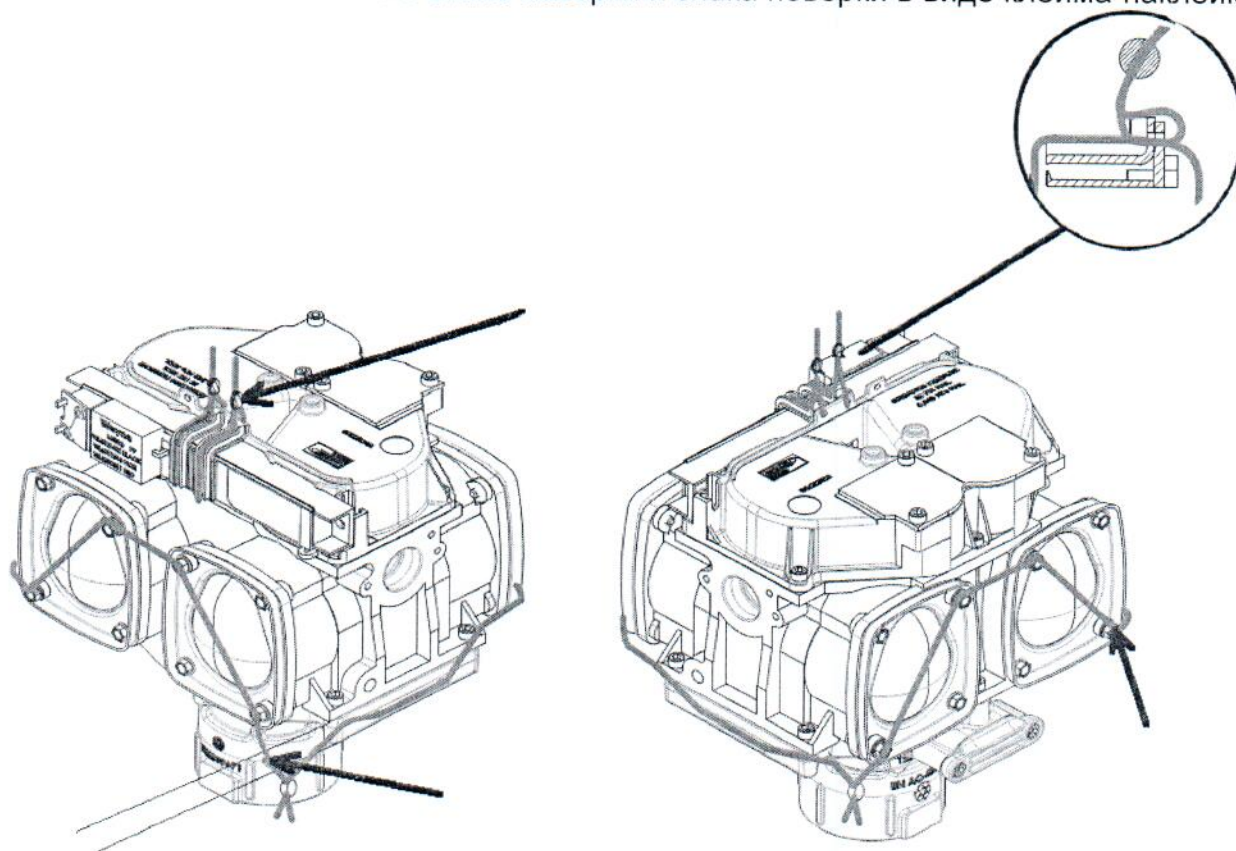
Схема нанесения знака поверки на iMeter
